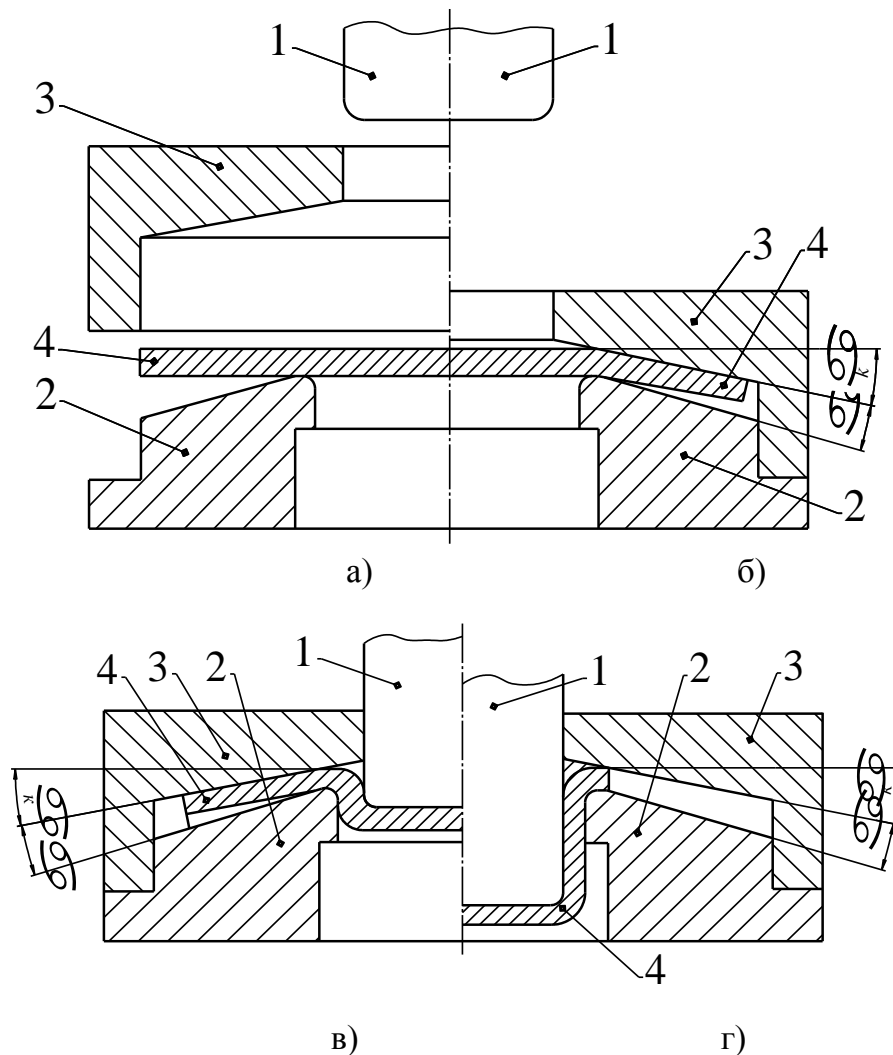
Схемы вытяжки полых изделий из листовой заготовки:
